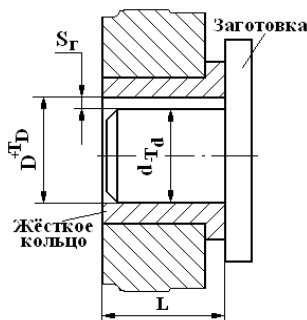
Схема базирования заготовки в жёсткое кольцо
